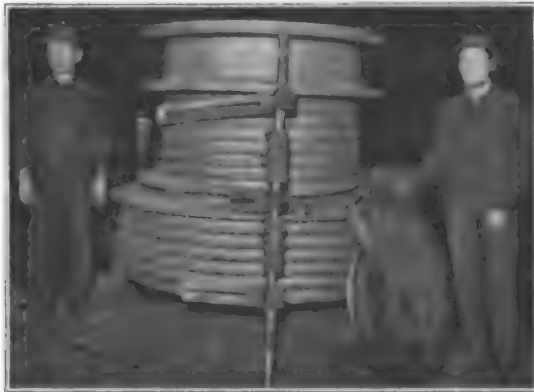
Seiltrommel mit spiralförmiger Rille.
